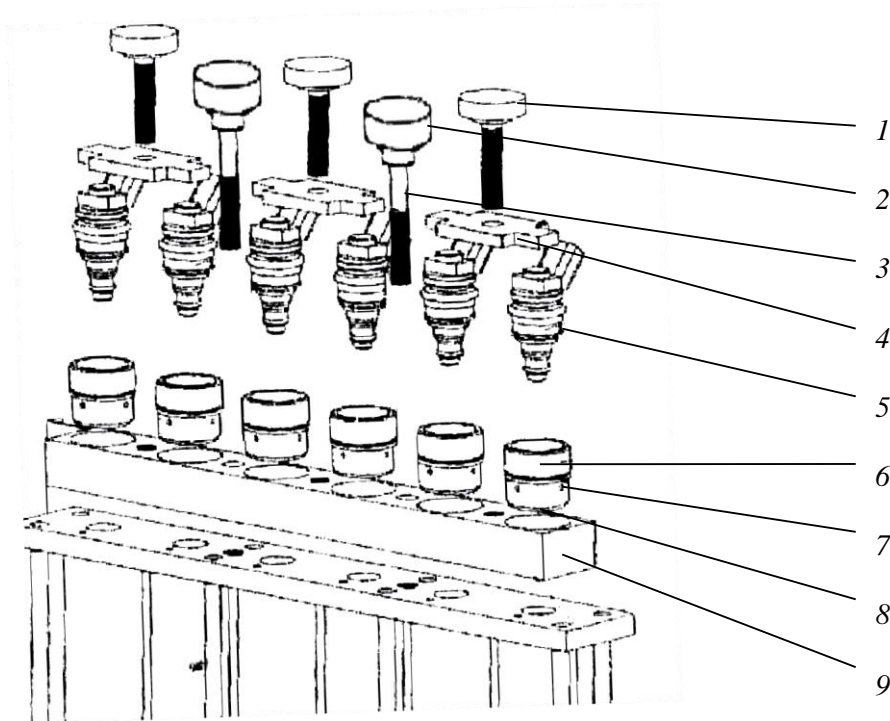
Схема установки форсунок с боковой подачей топлива:
